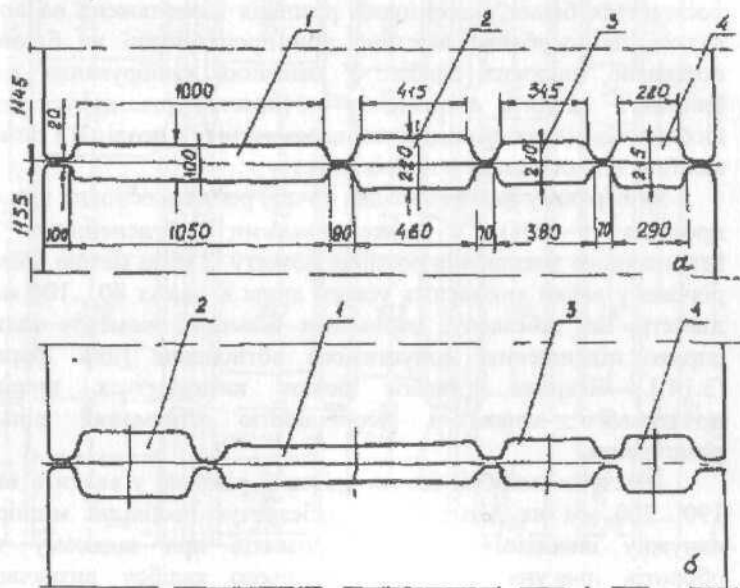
Схеми розташування калібрів : а - з гладкою бочкою з краю валка; б - в середині.
